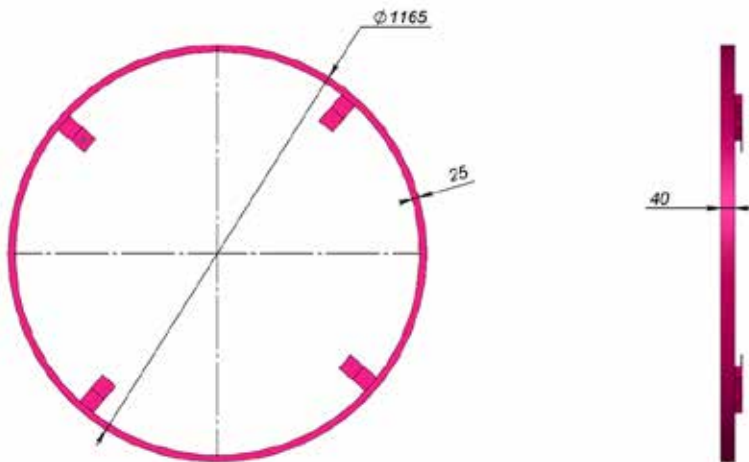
Кільцева рейка для обертання трекера за азимутом
